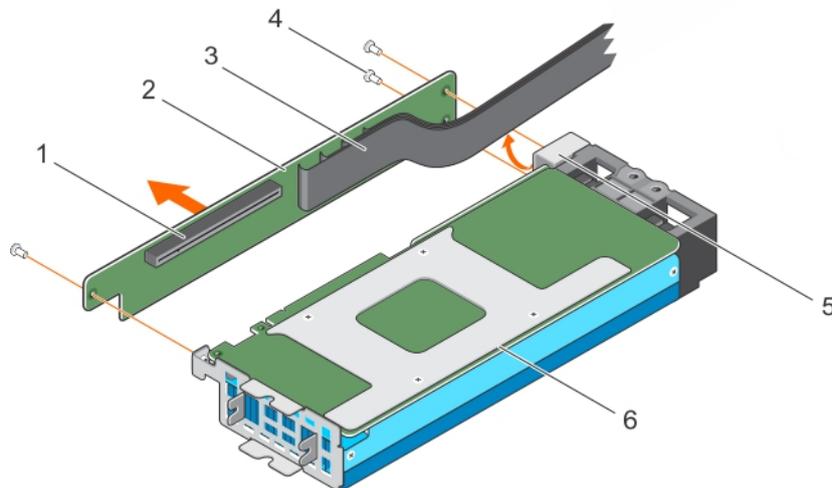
Extracción de la placa de cables del soporte vertical para GPU
